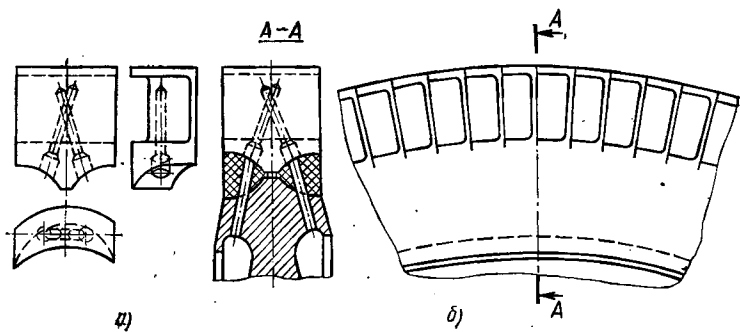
Обод рабочего колеса с приваренными лопатками:
